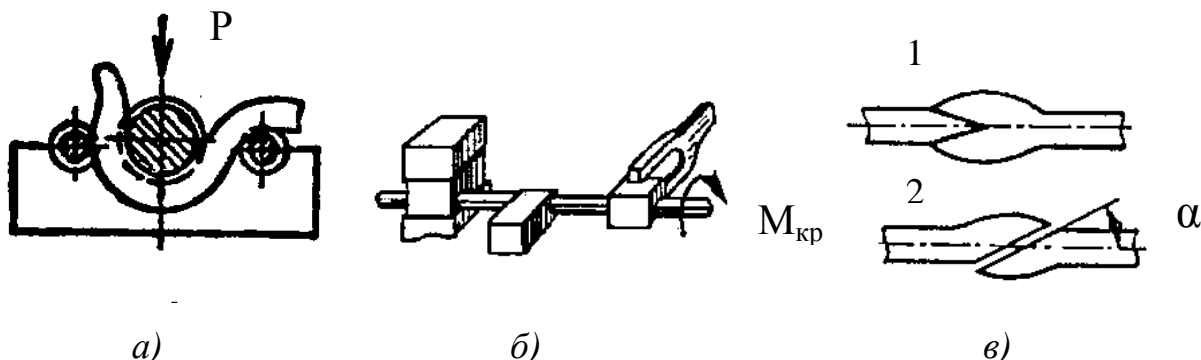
Операции свободнойковки: а – гибка, б – скручивание, в – кузнечная сварка (1 – в замок; 2 – внахлёстку); P – сила; $M_{кр}$ – крутящий момент; α – угол скоса кромок
